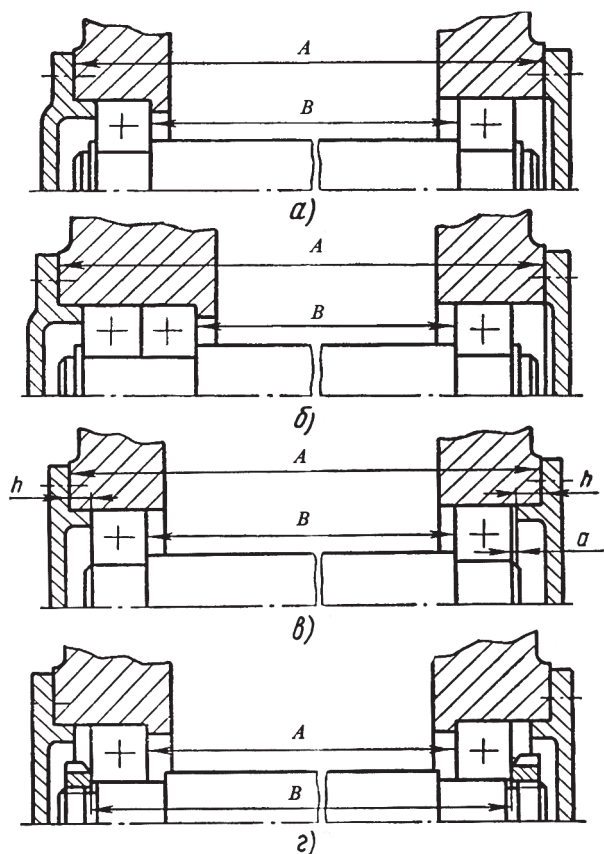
Схемы монтажа валов с подшипниками в корпус
